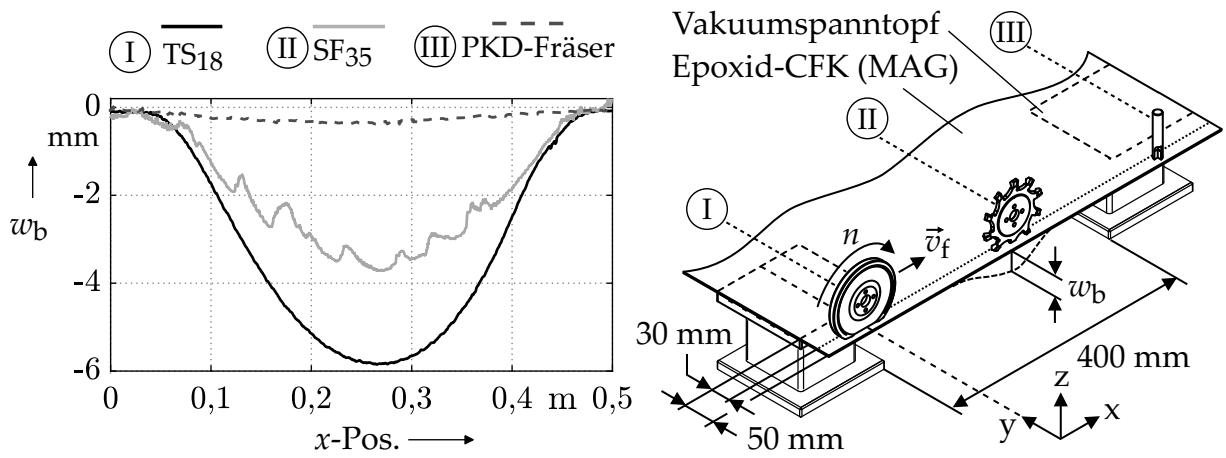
Abdrängung scheibenförmiger Werkzeuge im Vergleich zur Abdrängung konventioneller Schaftfräser
